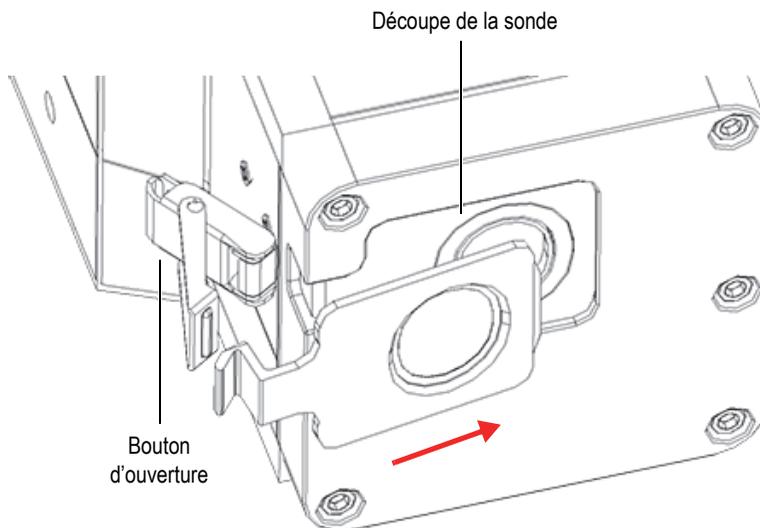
Positionnement de la plaque frontale sur la découpe de la sonde
